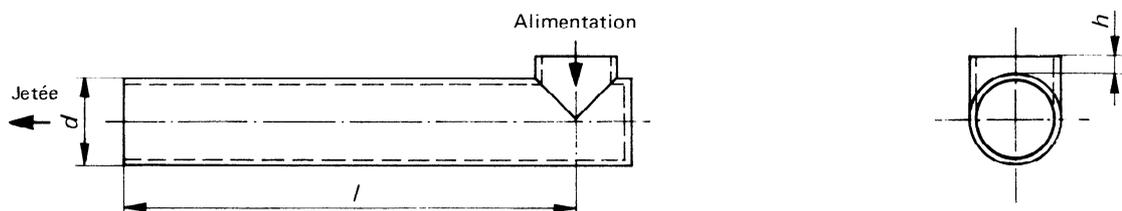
Auge tubulaire à une seule extrémité fermée
